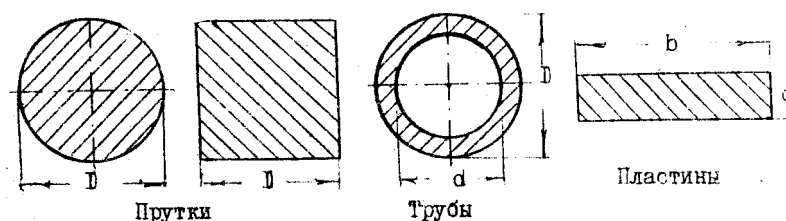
Виды свариваемых сечений при стыковой контактной сварке
